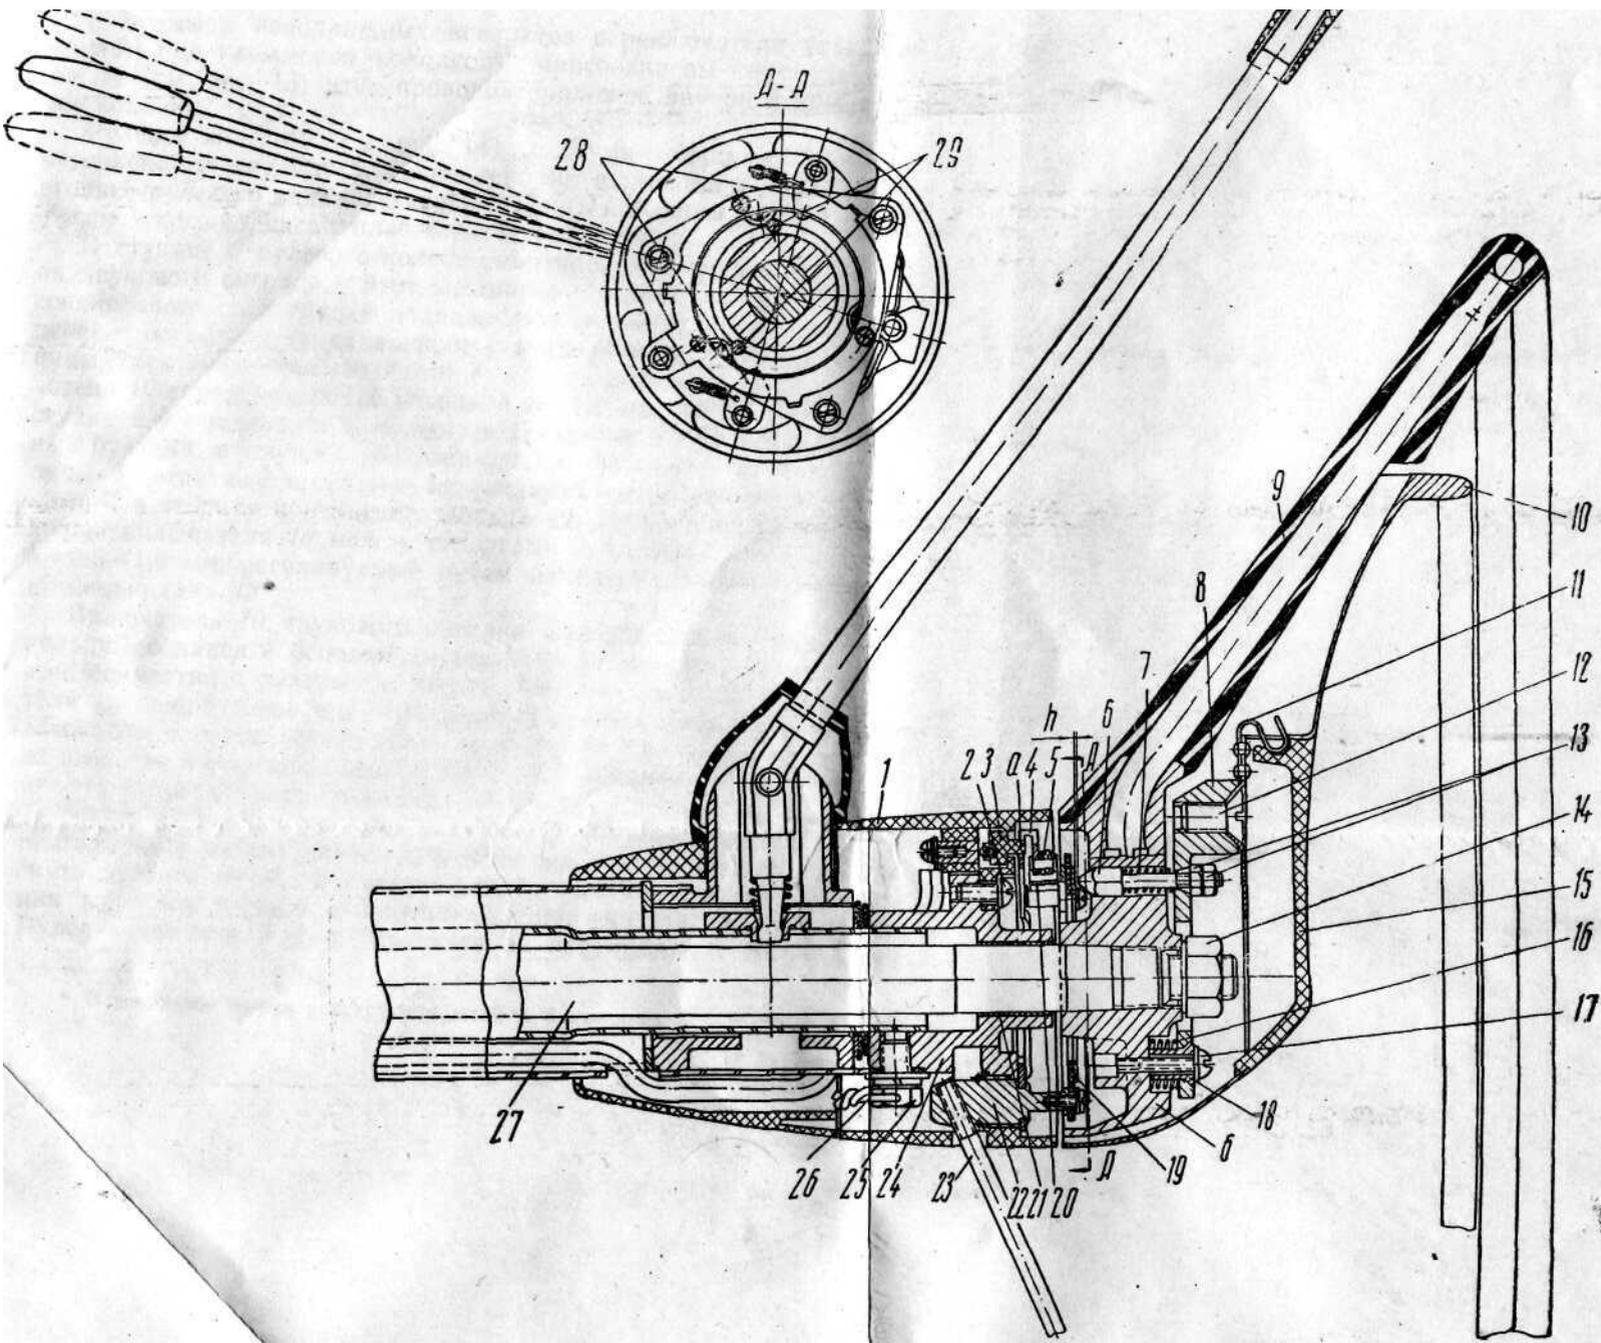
Установка верхнего конца рулевого вала, устройство переключателя указателей поворотов и крепление рулевого колеса:
